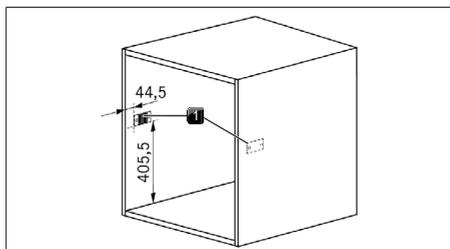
Nicho de montaje con placas de cierre del módulo
